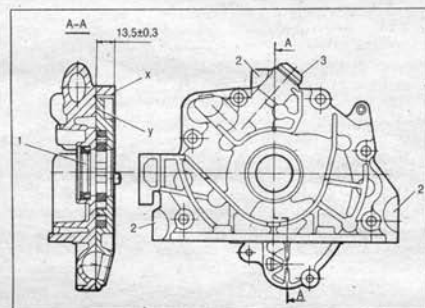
Точки крепления крышки масляного насоса при фрезеровании плоскостей:
